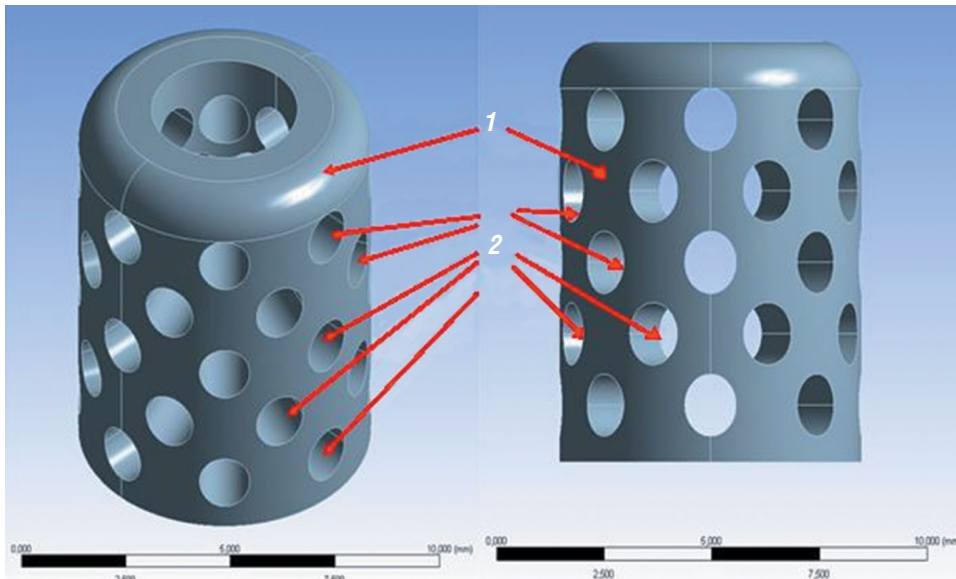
Цифровая 3D-модель реконструктивного цилиндрического имплантата: 1 — корпус костного имплантата; 2 — отверстия диаметром 1,2 мм
